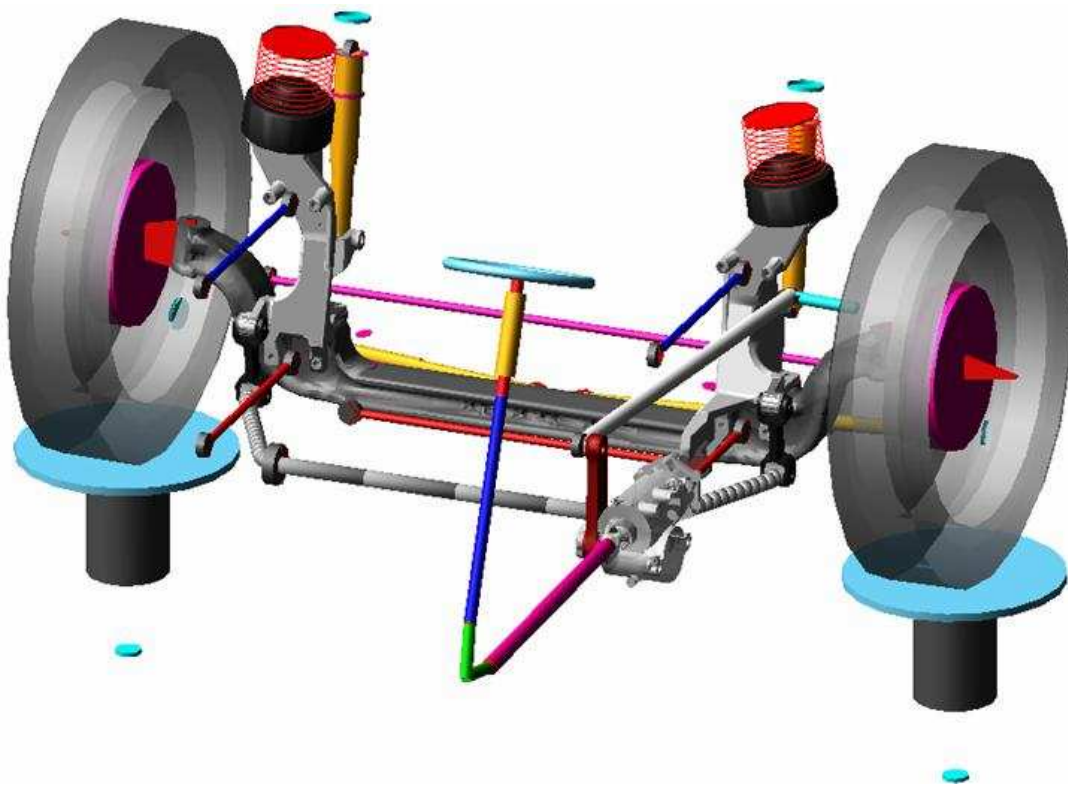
Montagem do teste da suspensão (*testrig*).
